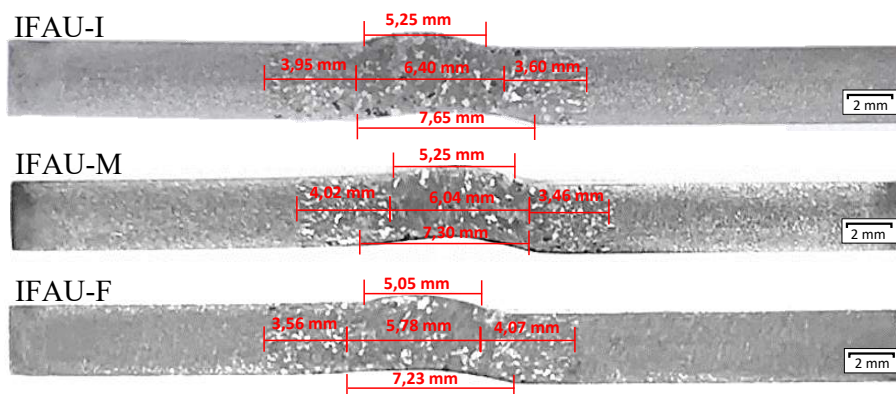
Dimensões das regiões de soldagem das amostras IFAU.
